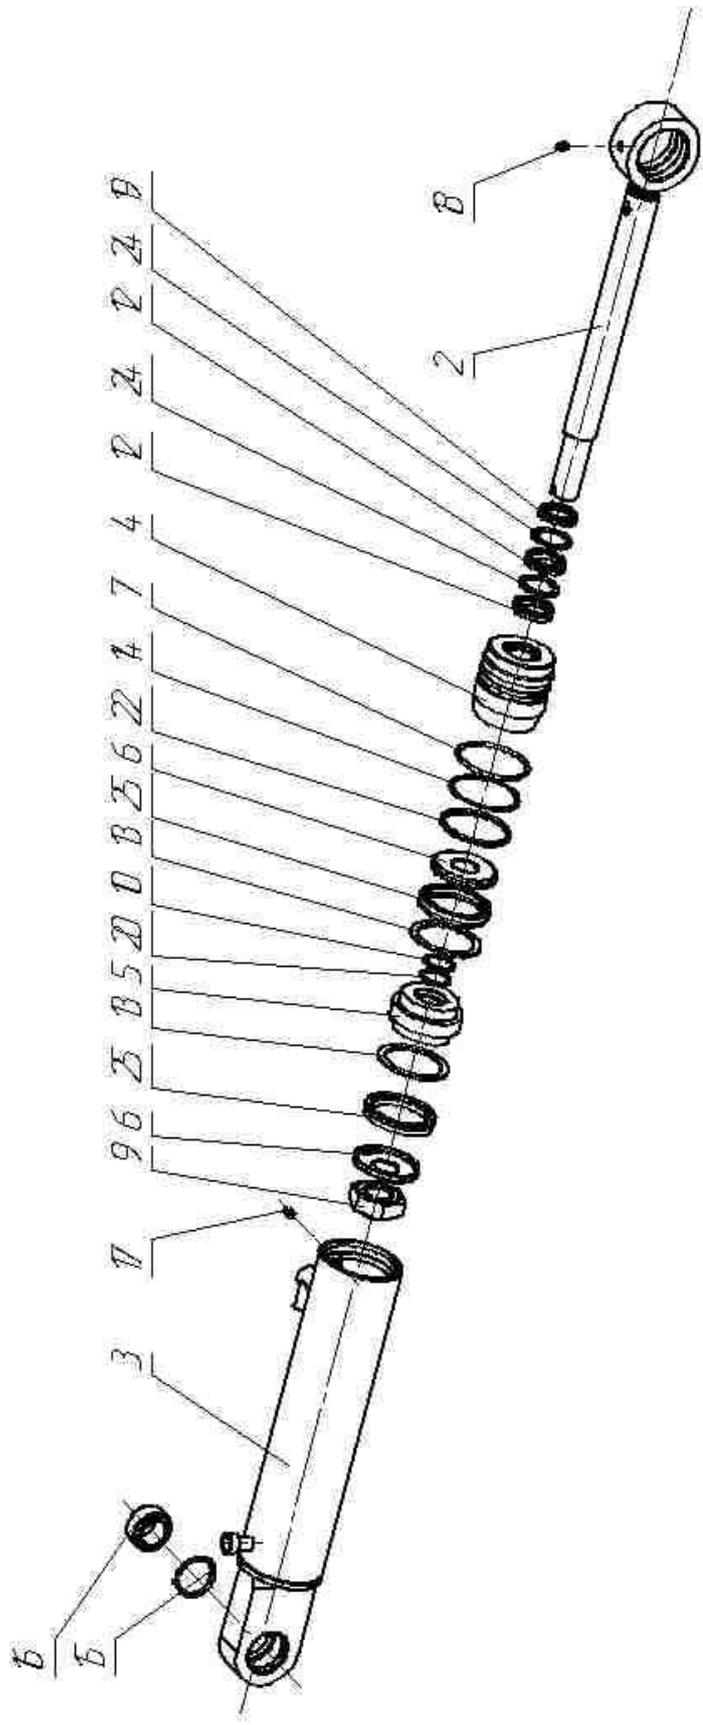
Гидрацилиндр паварота рабочего органа КРД-1,5.03.11.000
